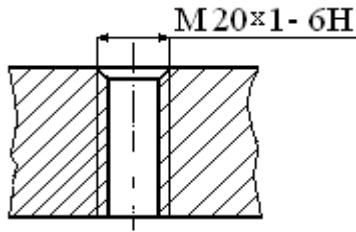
Обозначение внутренней резьбы на чертеже
